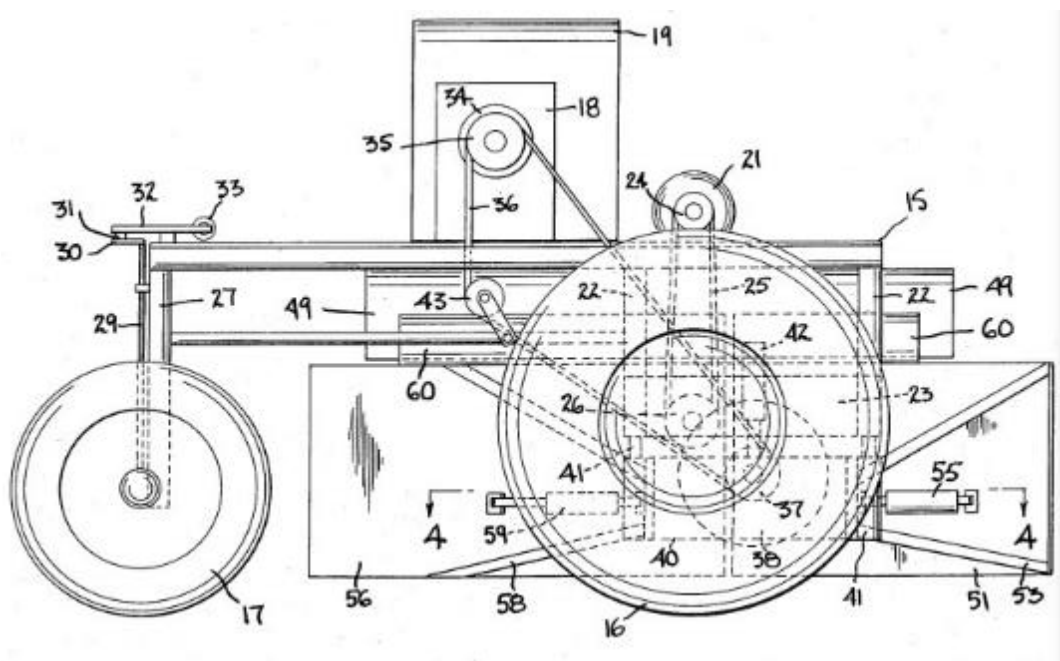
Вид збоку вдосконаленого пристрою: 15 – задній кінець рами; 16 – колесо; 18 – двигун; 19 – додаткова силова установка; 21 – енергопередавальна вісь; 22,27 – стійки; 23,38 – цапфа; 24,26 – зірочка; 25 – приводний ланцюг; 29 – штанга; 30 – верхні кривошипи; 31 – стяжка; 32 – важіль; 33 – шток гідроциліндра; 34 – вал відбору потужності; 35,37 – зірочки; 36 – передаточний ланцюг; 38 – барабан; 40 – опорний вузол; 42 – гідроциліндр подвійної дії; 43 – підпружинена натяжна зірочка; 44 – радіальні зуби; 51,56 – крила; 53 – розтяжка; 55,59 – гідравлічний циліндр; 58 – розкіс;
